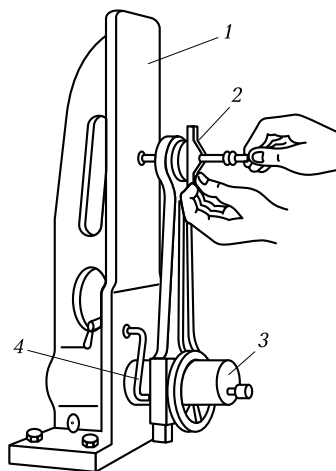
Приспособление для контроля шатуна на двойной изгиб:
